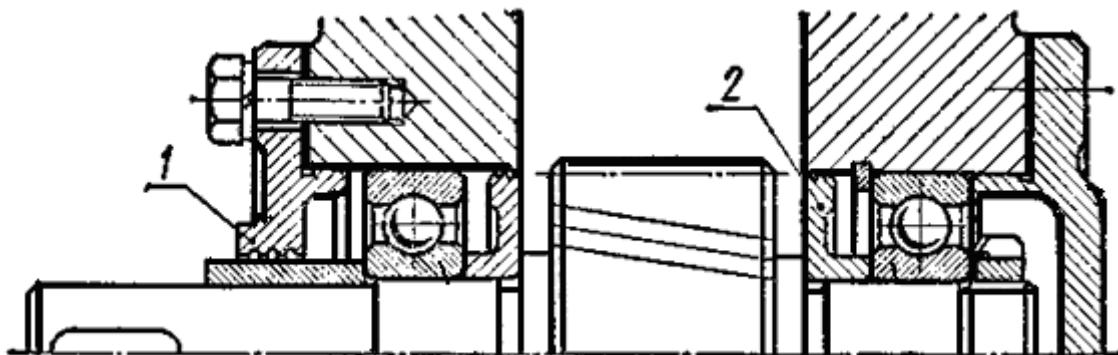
Вал в сборе: 1 – крышка с уплотнением; 2 - мазеудерживающее кольцо
